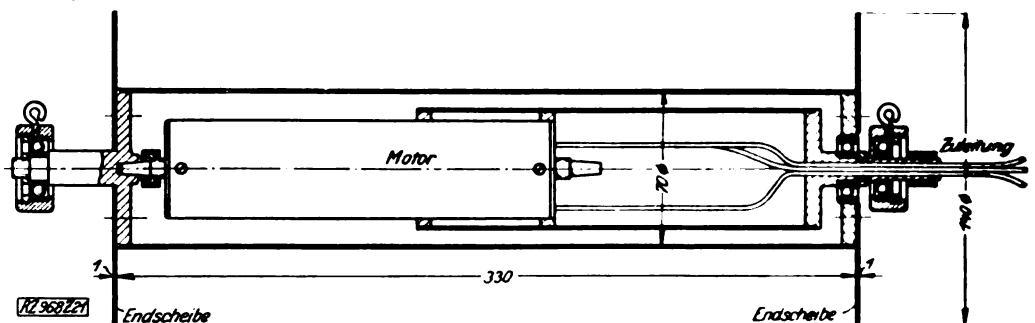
Umlaufende Walze mit eingebautem Motor für die genaueren Messungen im Windkanal.
